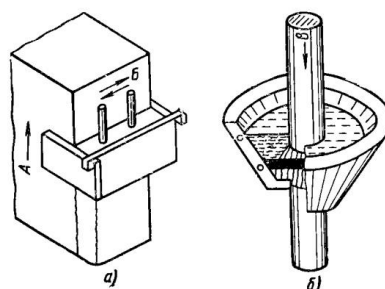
Схемы электрошлаковой наплавки (а) и контактной шлаковой сварки (б).
